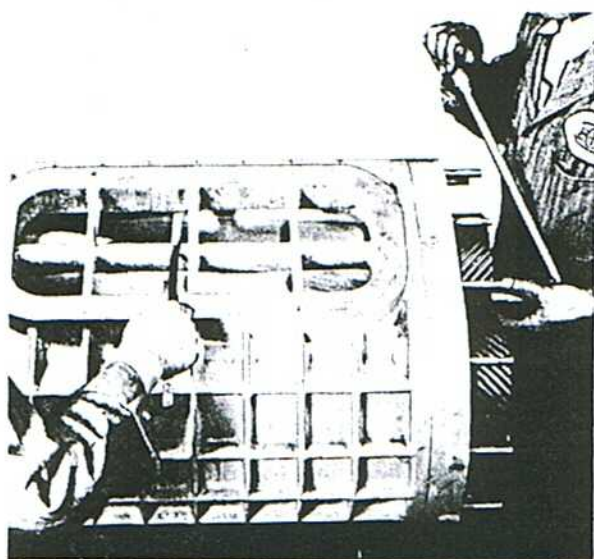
Comprobación del juego entre rotor y carcasa.
